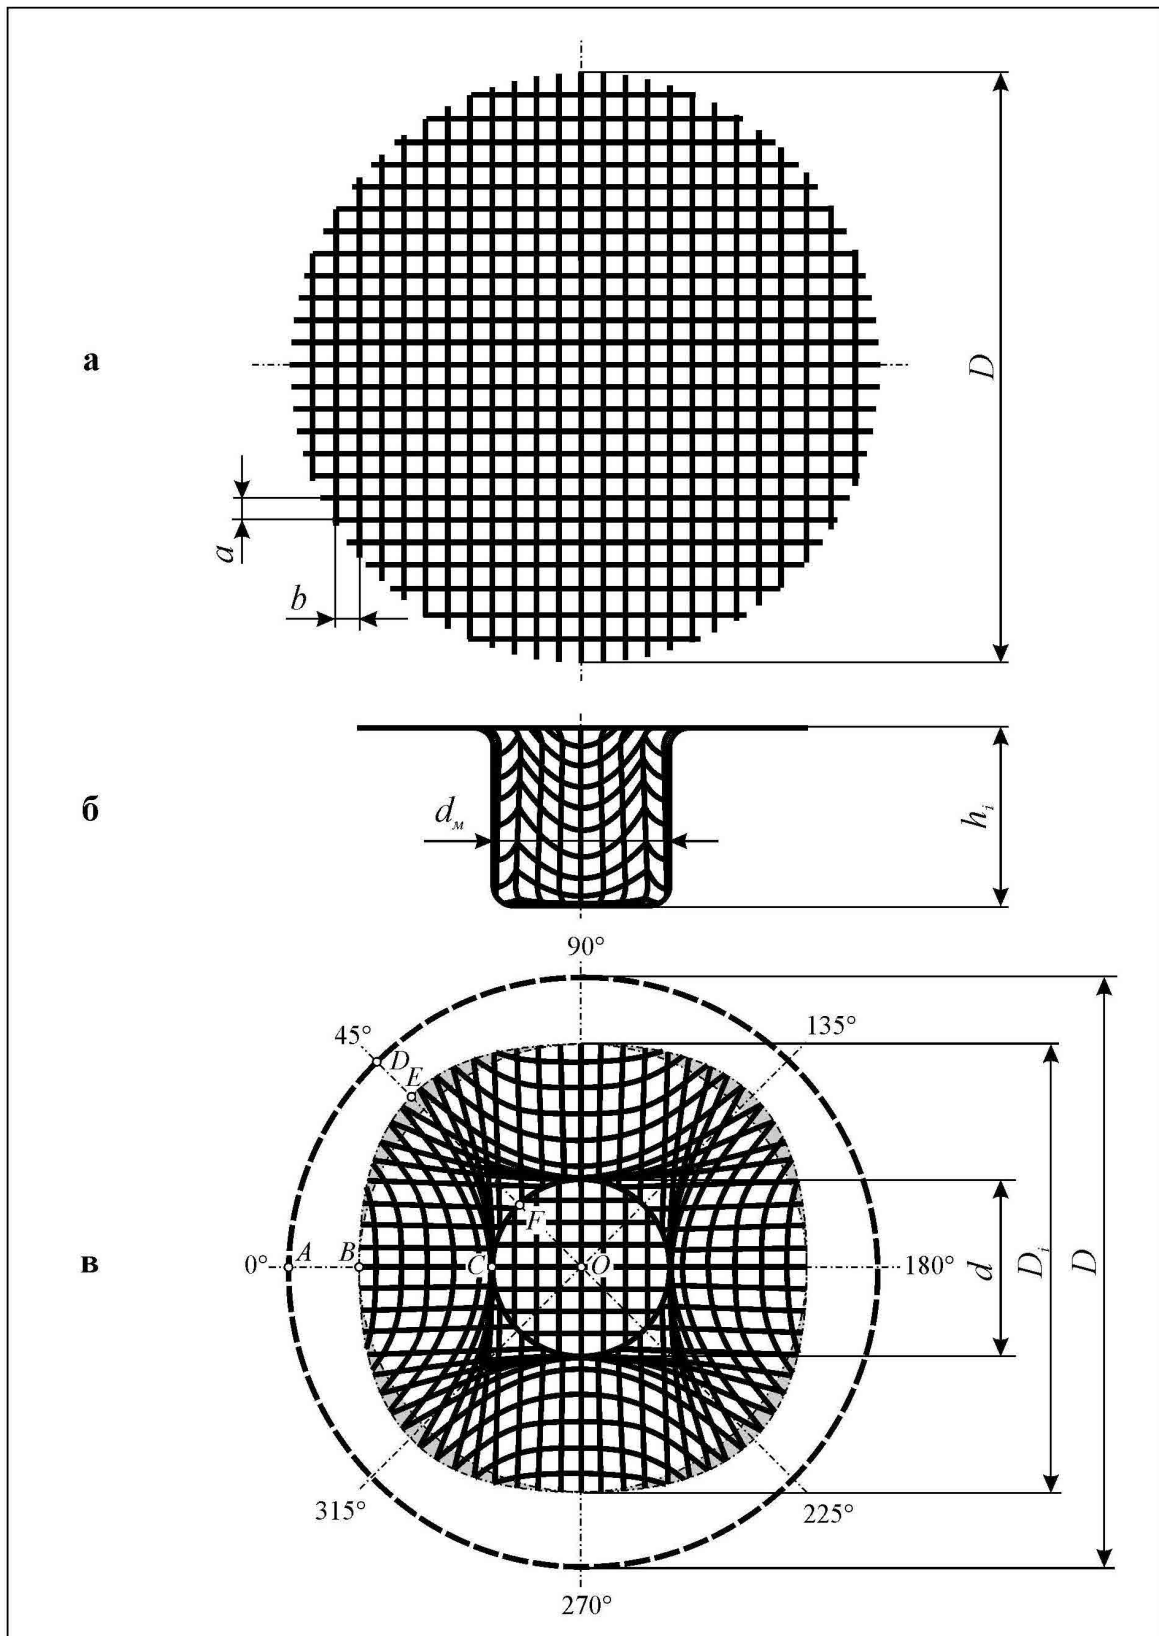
Технологічна схема формоутворення поверхні тіла при витягуванні з притиском фланця із плоскої сітчастої заготовки
